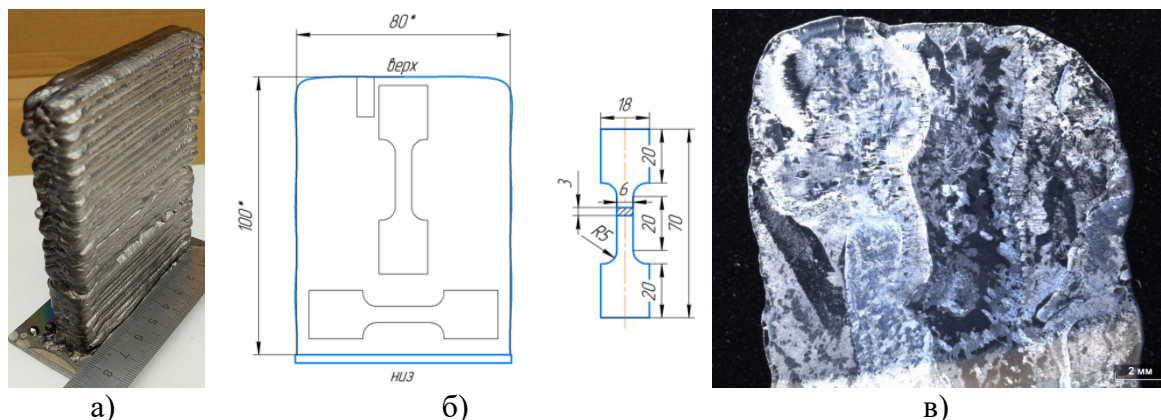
Фотография наплавленной стенки (а) со схемой разрезки (б) и макрошлифом поперечного сечения (в)
